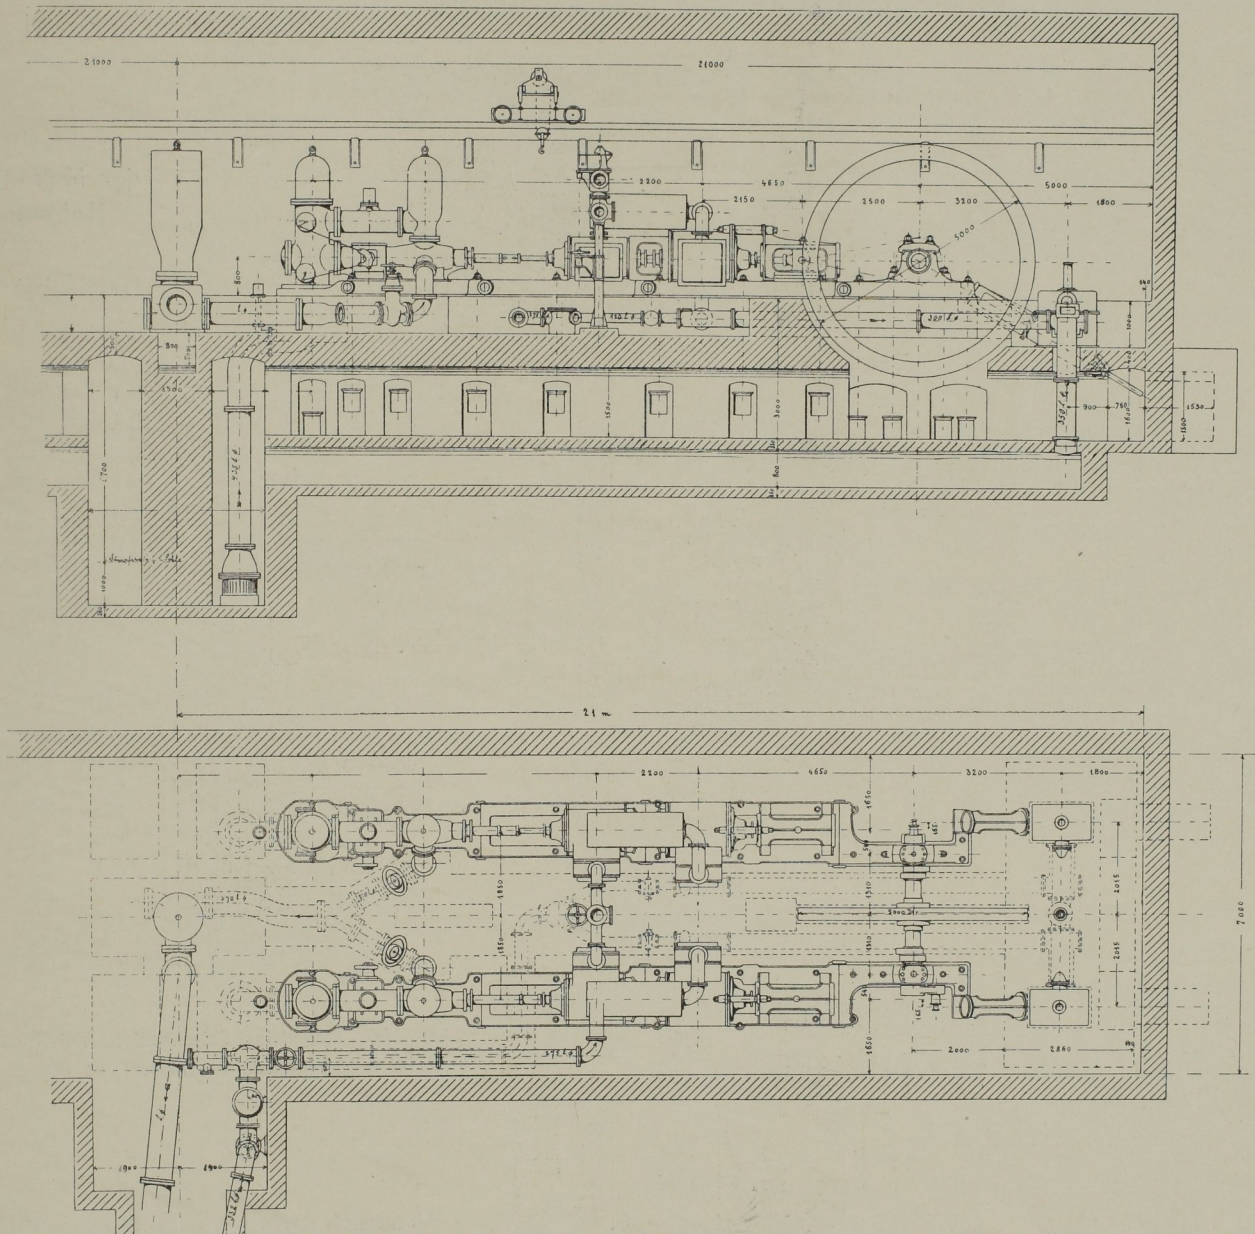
Seitenansicht und Grundriss. Massst. 1:150.
